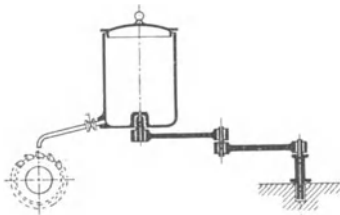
Ungünstige Zuführung des Kühlmittels.
